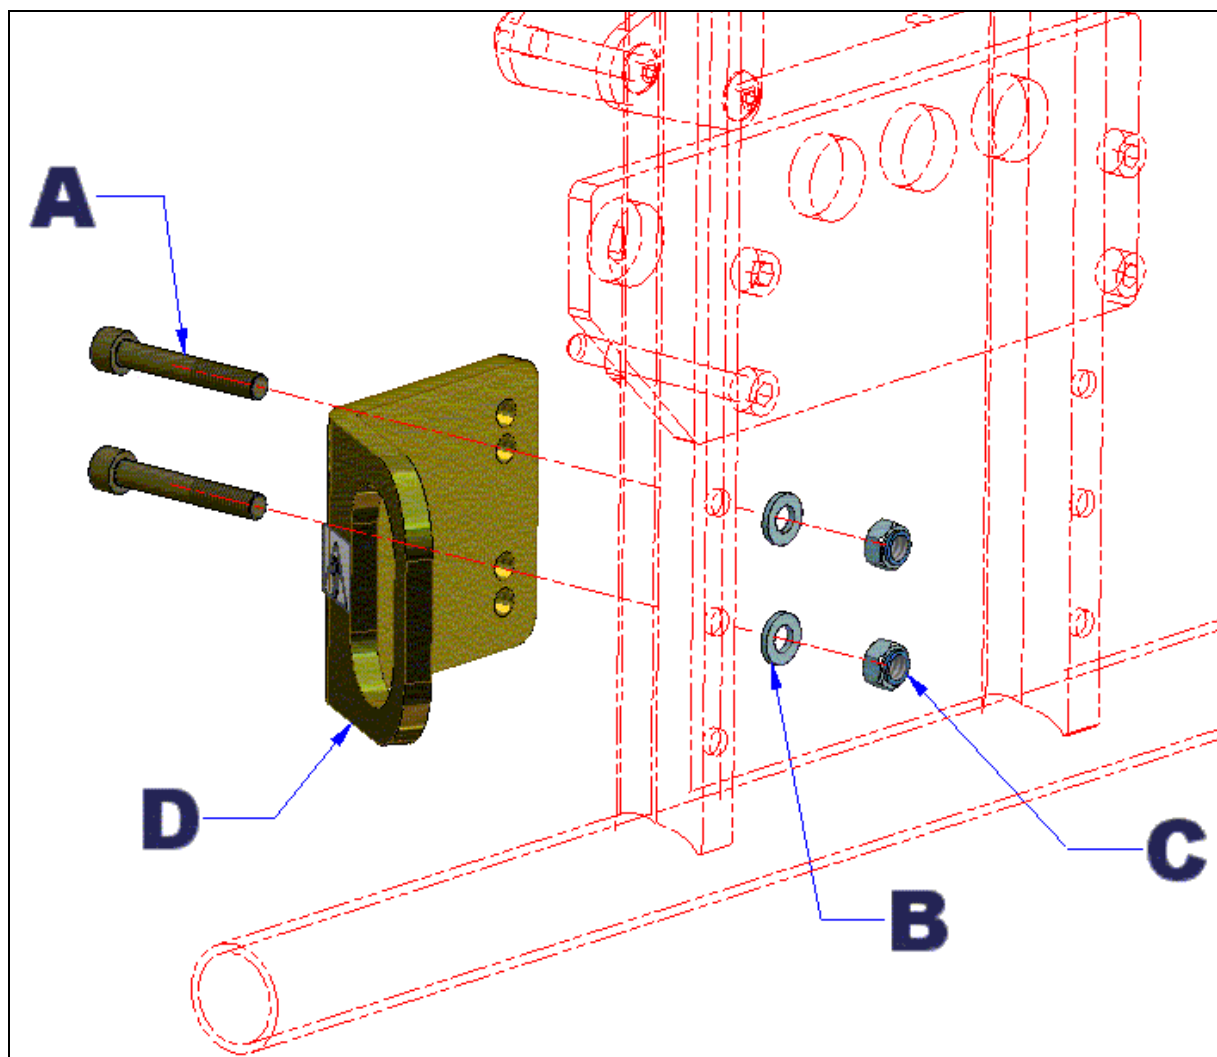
B : Installation des anneaux d'ancrage ARRIÈRE.
